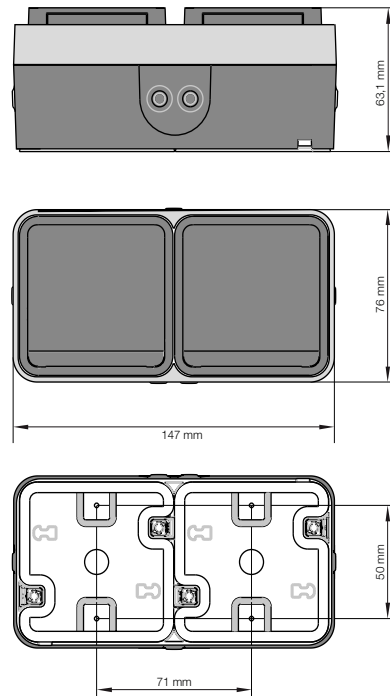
Steckdose SCHUKO 2fach mit Klappdeckel
